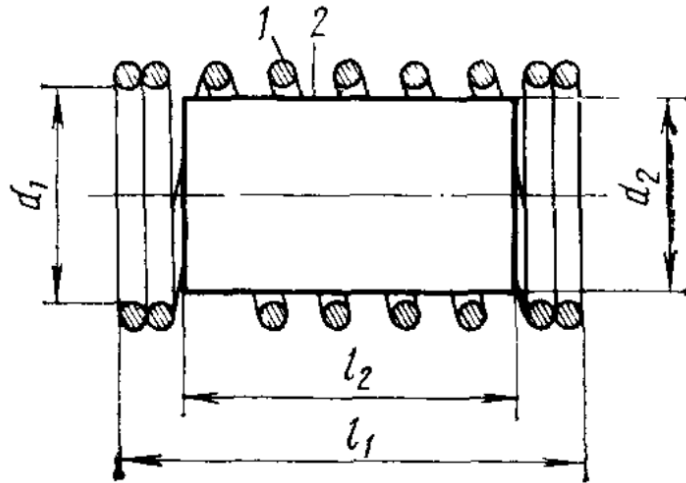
Циліндричний індуктор: 1 – індуктор; 2 – деталь
